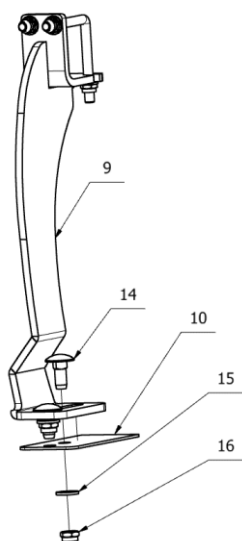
Wał packer $\varnothing 510\text{mm}$ – mocowanie belki ze skrobakiem w części bocznej.
